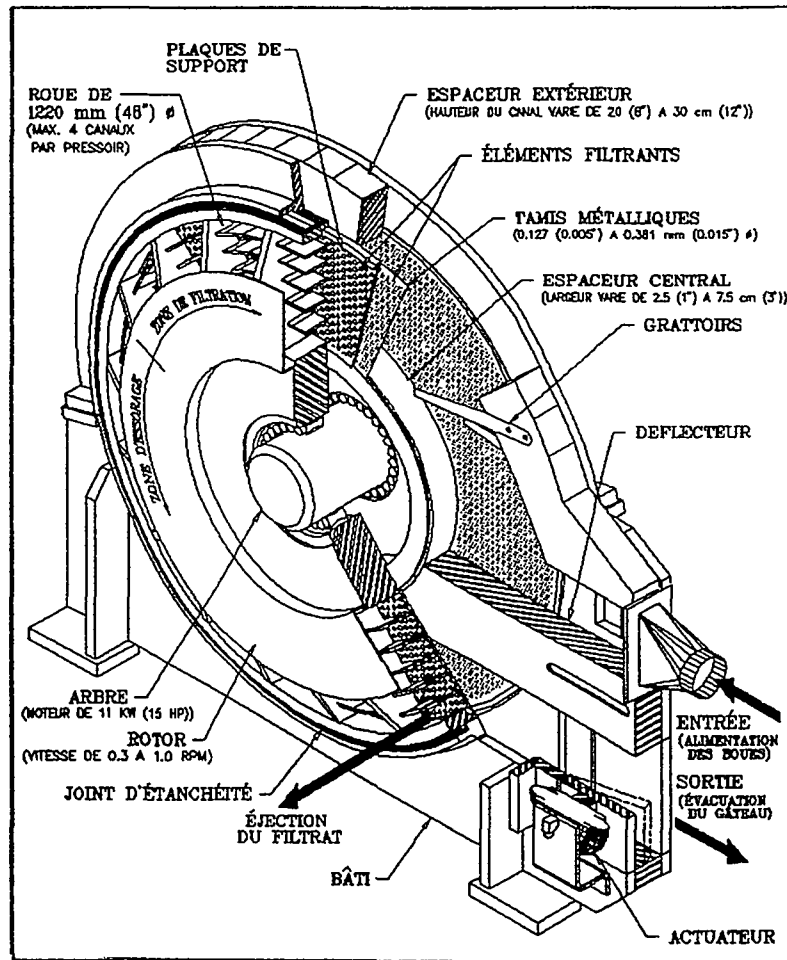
Vue isométrique des composantes mécaniques du presseur rotatif
